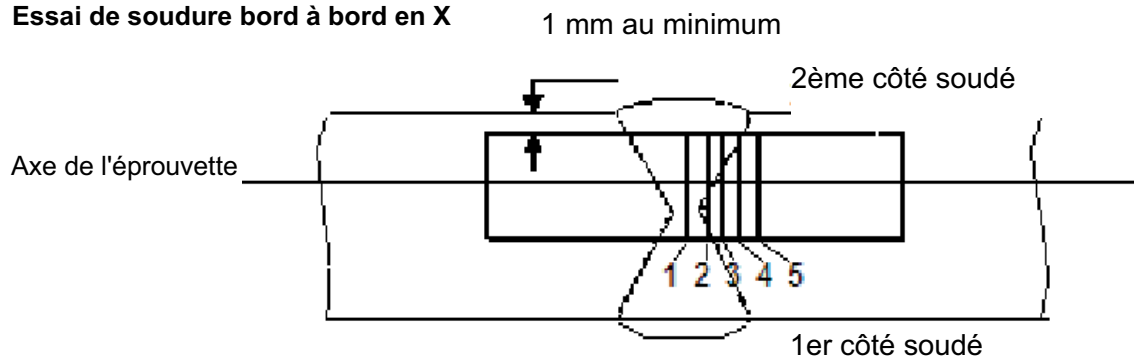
Orientation de l'éprouvette utilisée pour les essais de soudure
